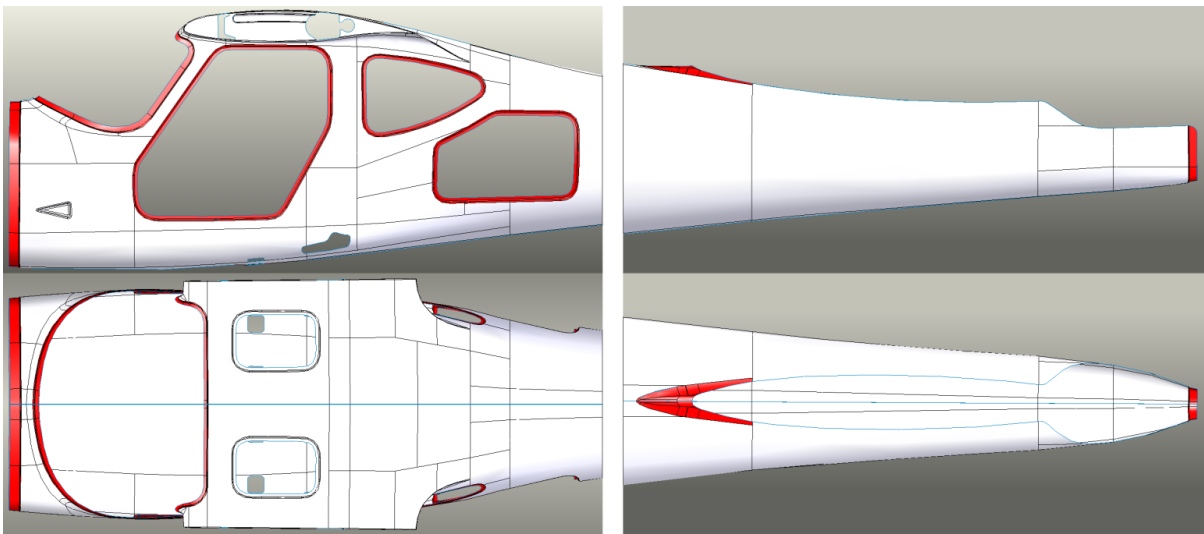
Faces enlevées à l'avant et à l'arrière (vue de côté et de dessus)
